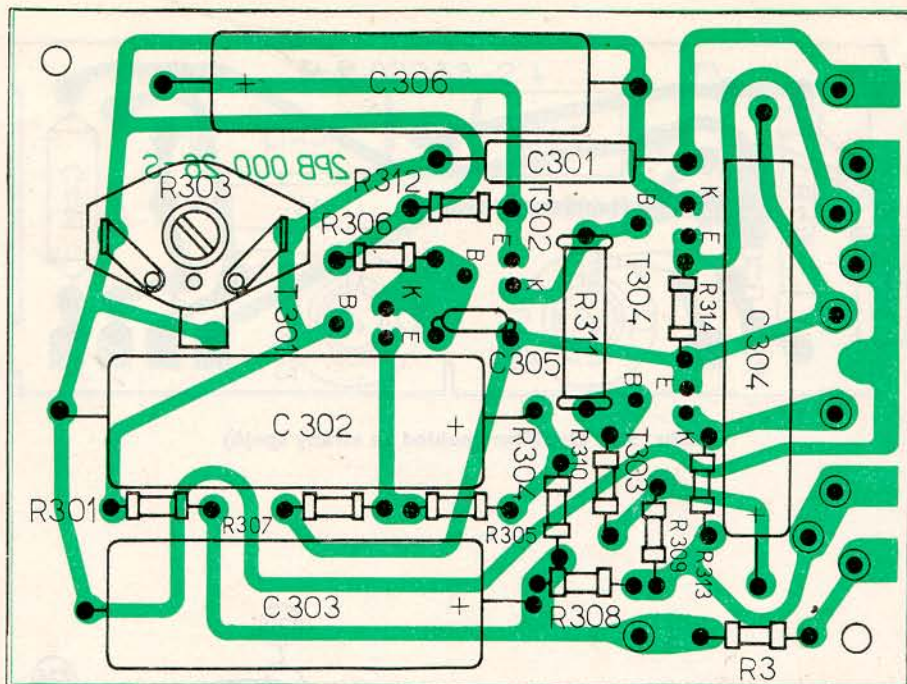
Deska korekčního zesilovače (pohled ze strany spojů)
